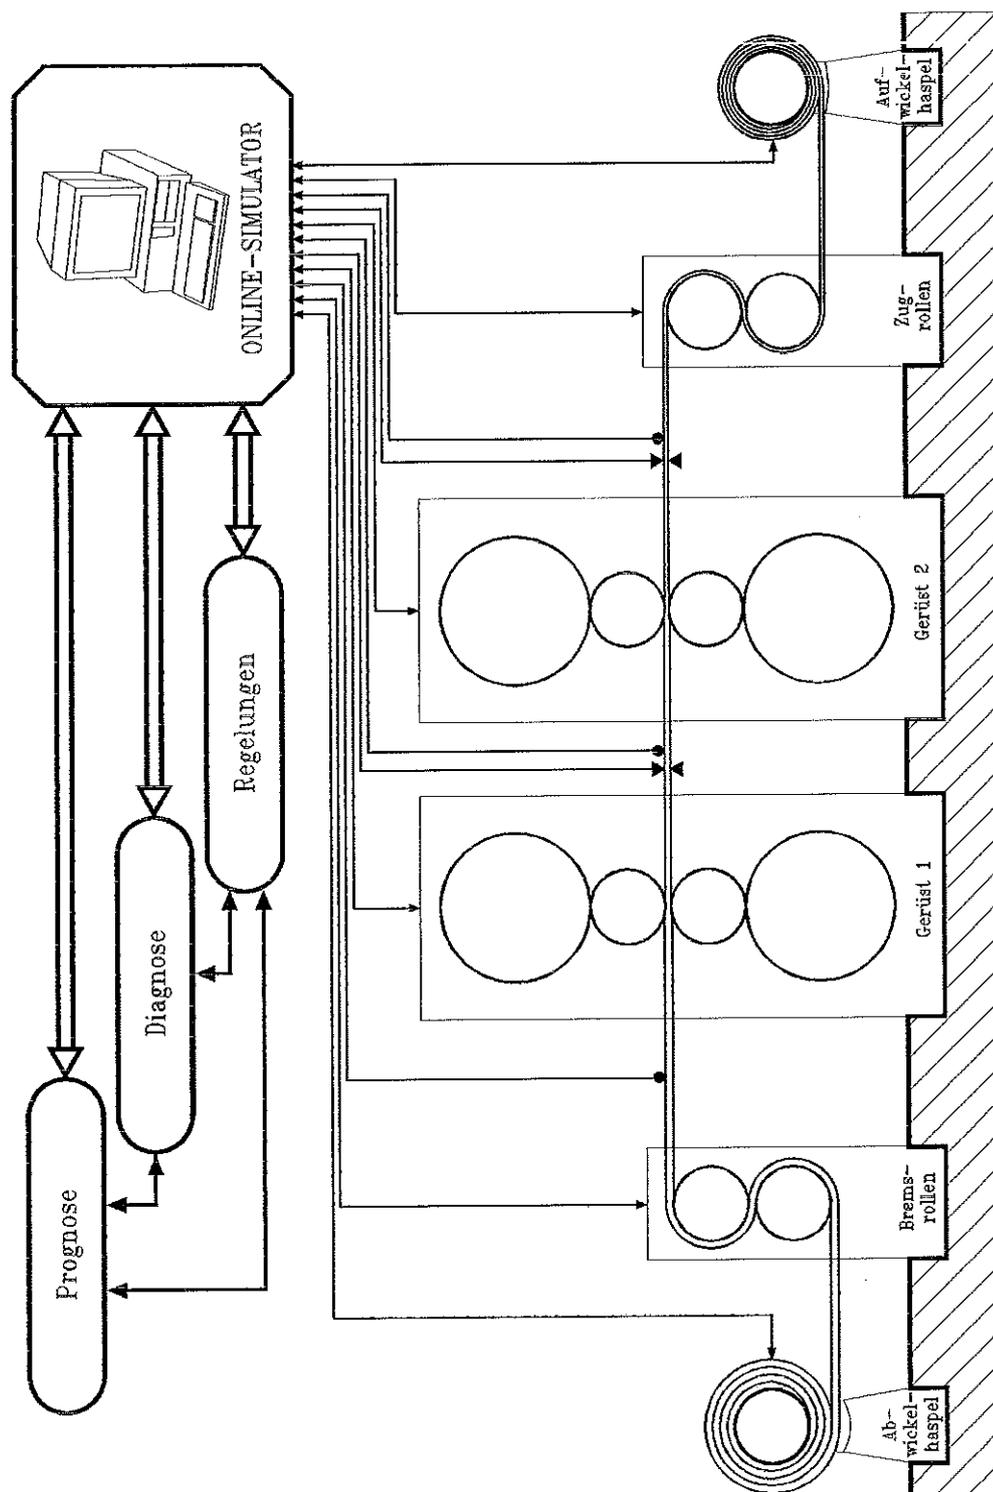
Geplanter Einsatz eines Online-Simulators an einer zweigerüstigen Walzstraße
